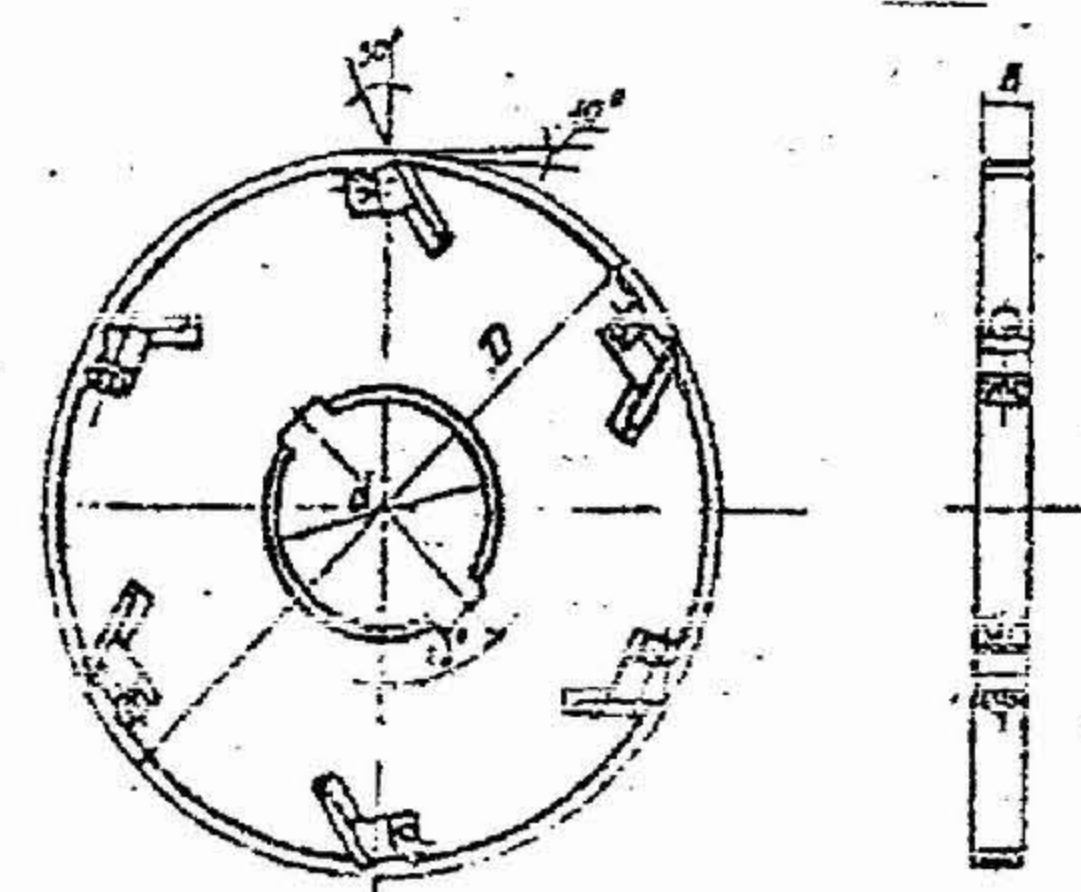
Фреза: 1-корпус; 2-резец; 3-гайка; 4-винт; 5-регуляровочный винт; 6-защелка
